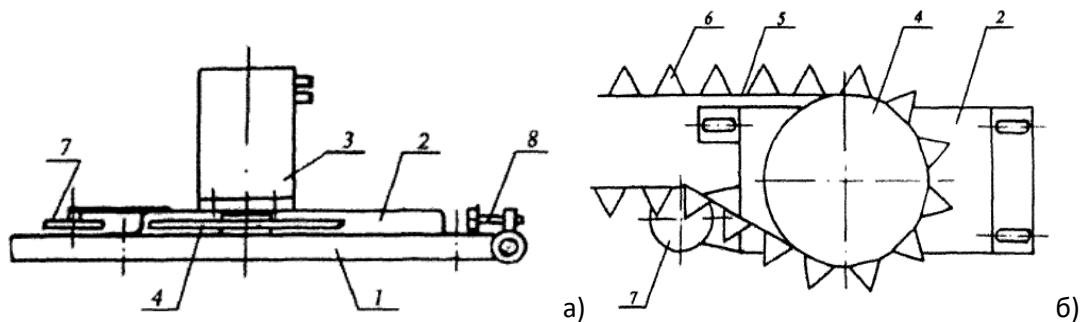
Схема привода косарки: а – вид з переду, б-вид зверху
